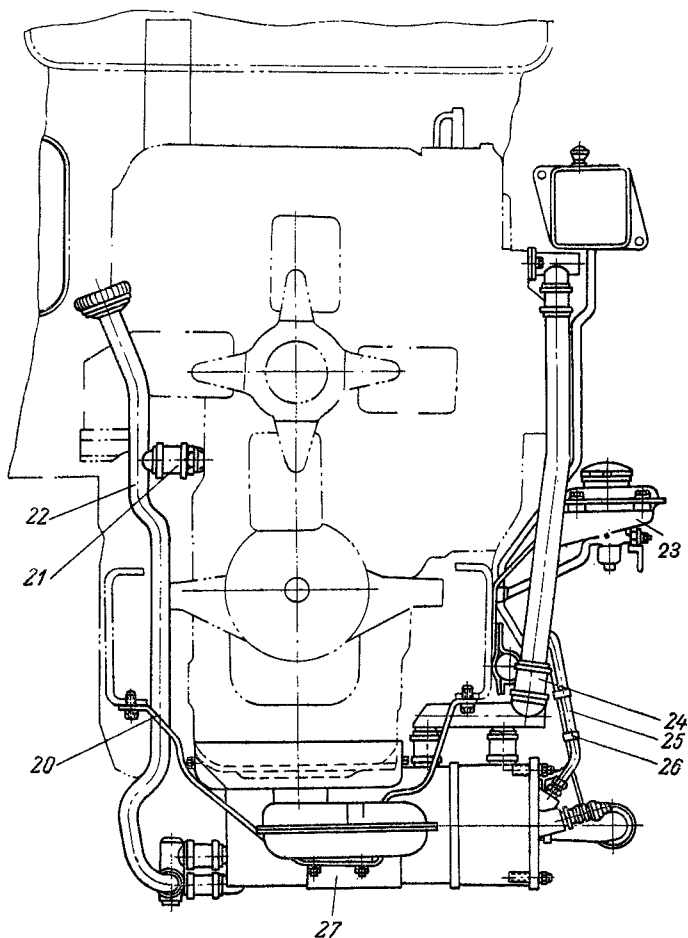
Установка предпускового подогревателя ПЖБ-200Б (вид слева).
